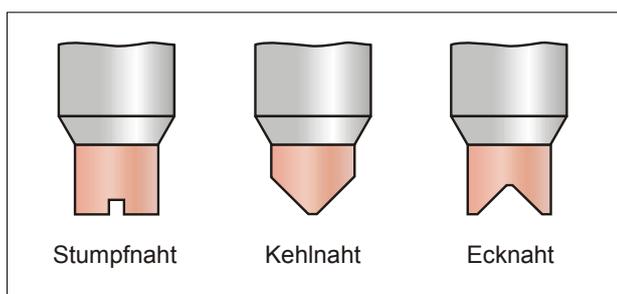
spotArc-Punktschweißbrenner, wassergekühlt
